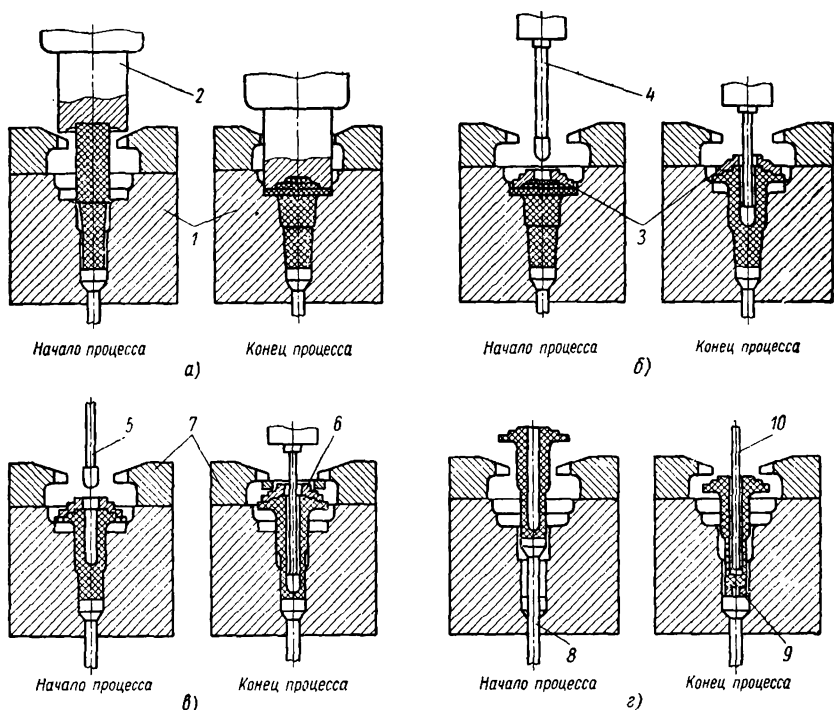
Схема процесса штамповки втулки: а — штамповка фланца; б — предварительная прошивка; в — окончательная прошивка; г — пробивка дна
